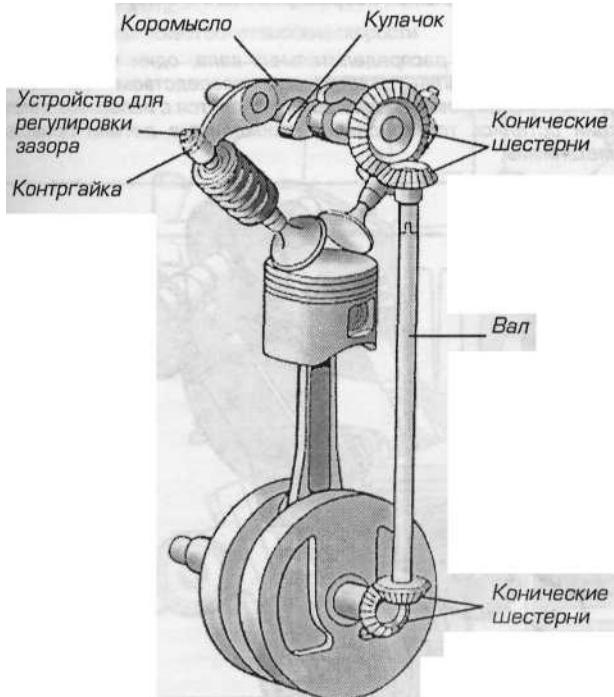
г Устройство механизма газораспределения с одним верхним распределительным валом, привод которого осуществляется при помощи пары конических шестерен и вала
